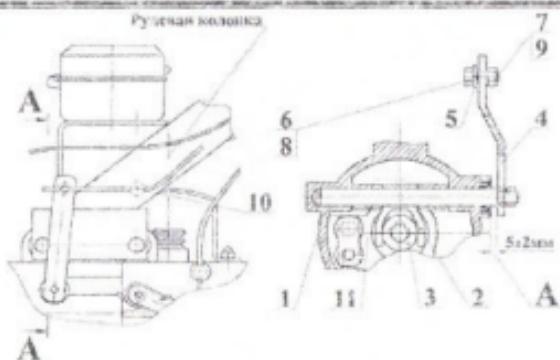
Коробка передач. Положение рычага сцепления.
